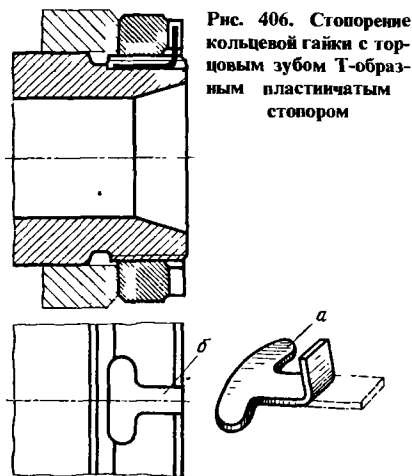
Стопорение кольцевой гайки с торцовым зубом Т-образным пластинчатым стопором
